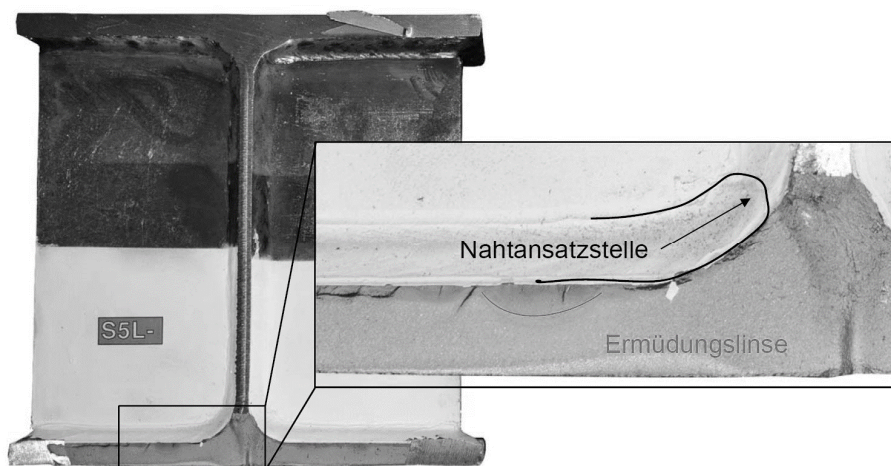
Bruchfläche mit Ermüdungsanriss und Nahtansatzstelle
